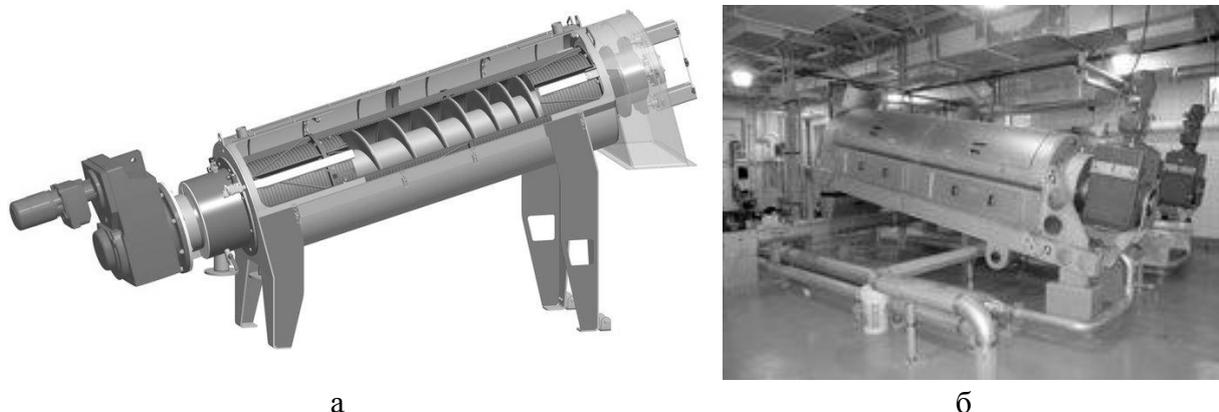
Короотжимной пресс: схема (а) и фотография (б)
